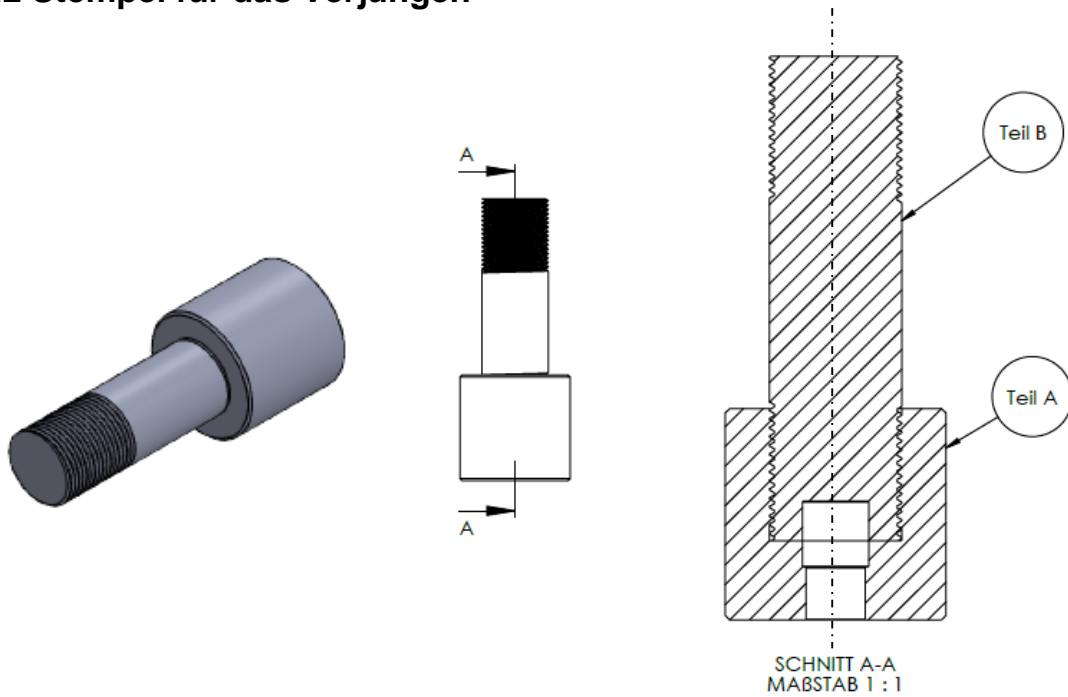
Technische Zeichnung des Stempels für das Verjüngen.
